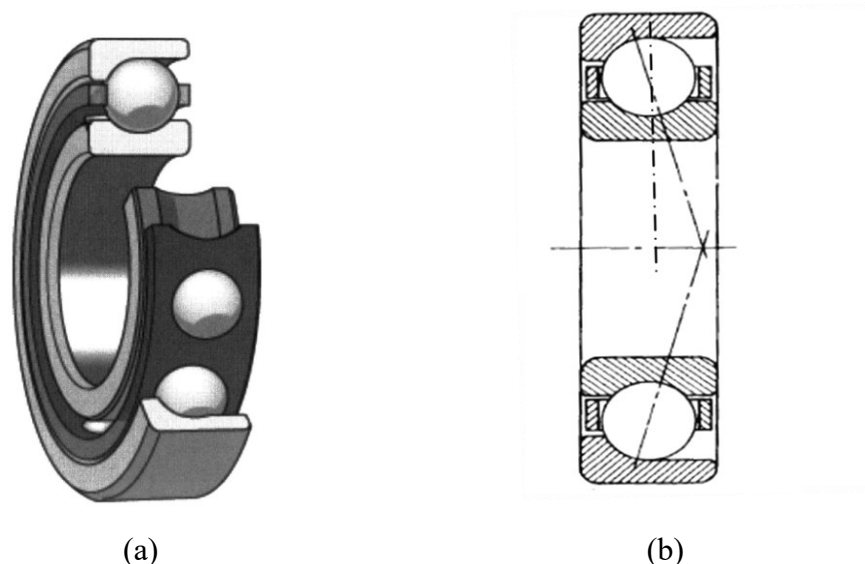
(a) Rulment radial-axial cu bile (a) și o secțiune printr-un rulment radial- axial cu bile (b)
